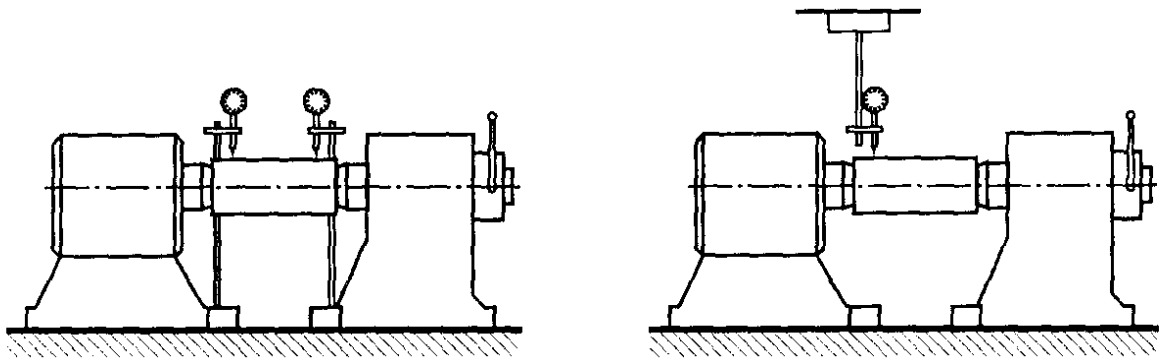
Контроль точности центров бабок зубошевинговального станка
